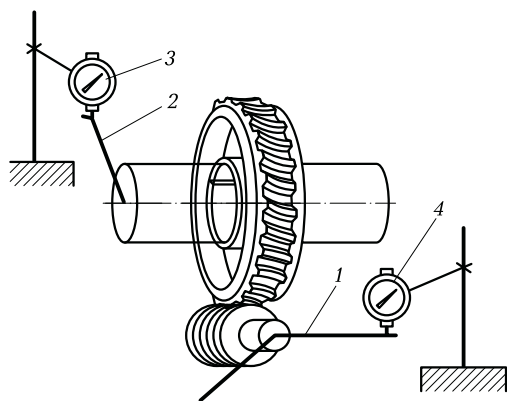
Схема контроля бокового зазора в червячной передаче:
